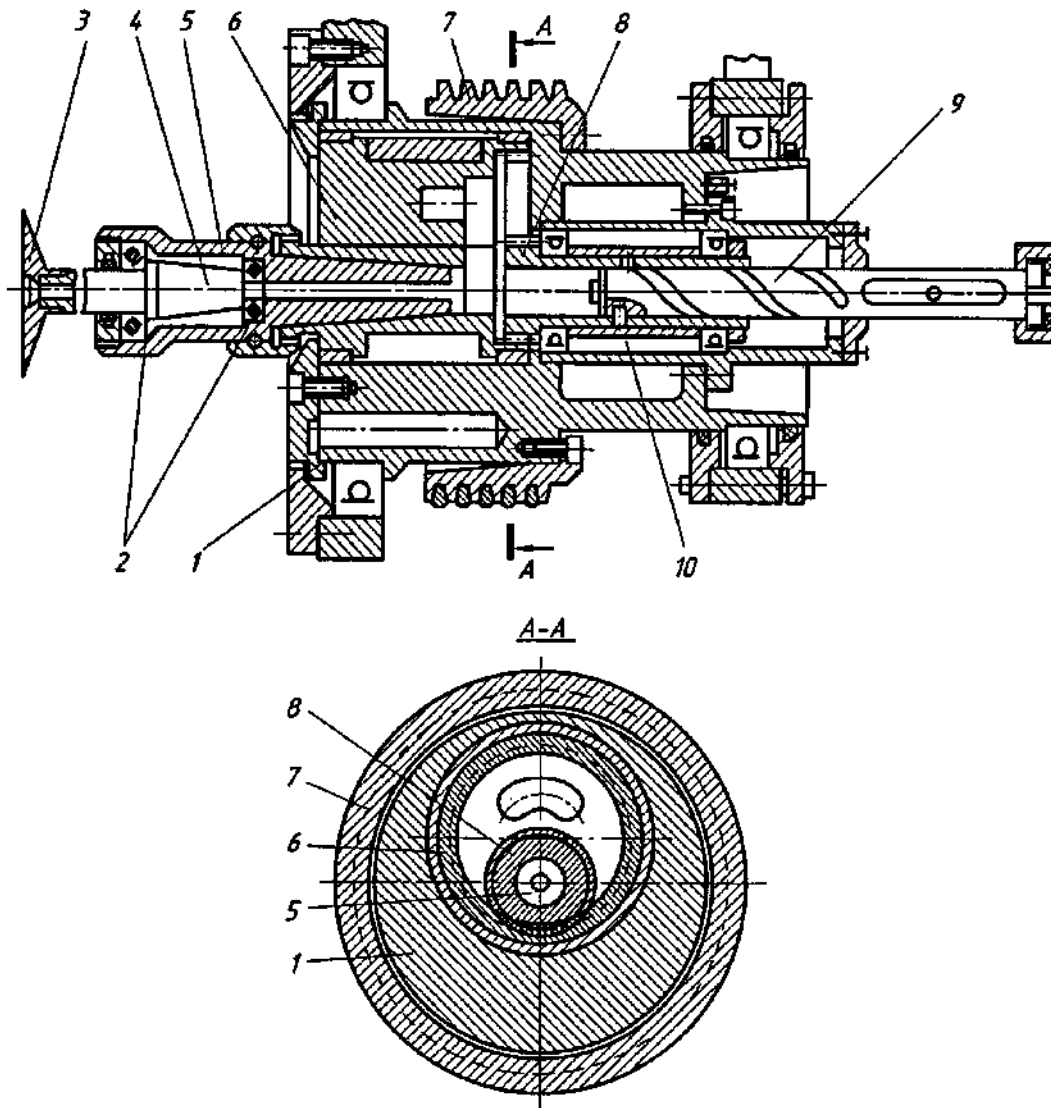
Схема конструкции отрезного устройства станка СО-3М:
